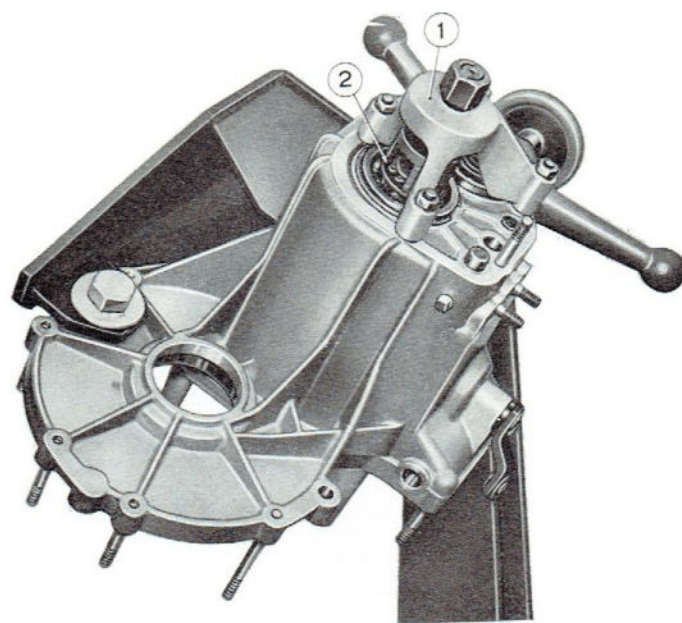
Anordnung des Werkzeugs A. 70106/1/2 für Ein- und Ausbau der Tellerfedern und des Sicherungsrings für die Vorgelegewelle.
